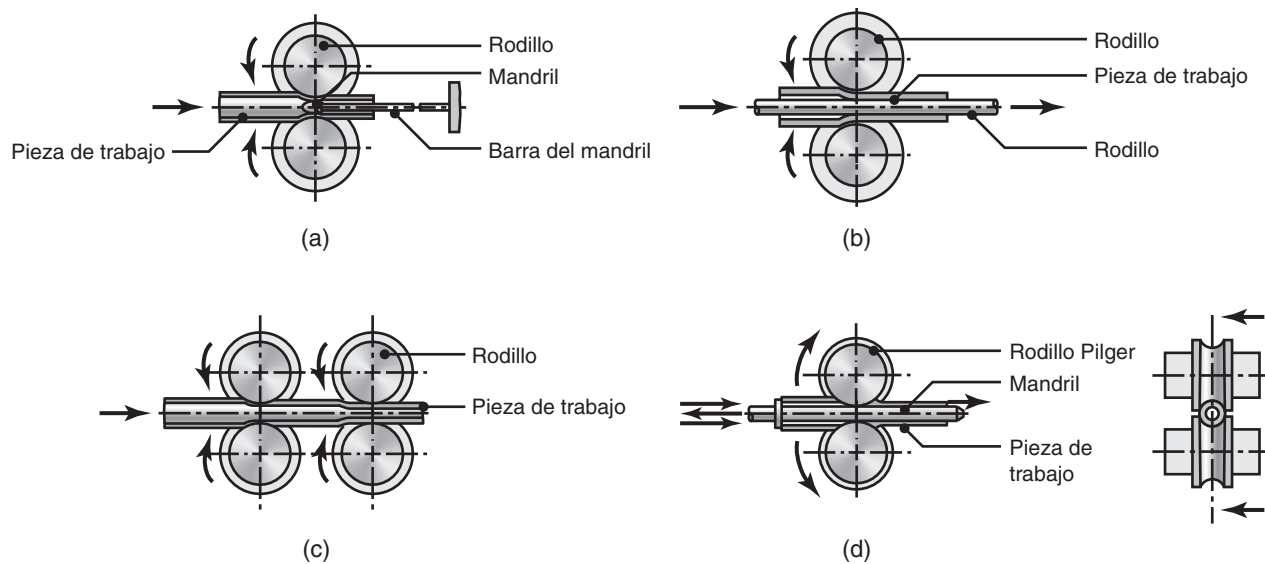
Esquema de diferentes procesos de laminado de tubos: (a) con mandril fijo; (b) con mandril flotante; (c) sin mandril, y (d) laminado Pilger con un mandril y un par de rodillos de forma. También se pueden cambiar los diámetros y espesores de los tubos mediante otros procesos, como estirado, extrusión y torcido.
